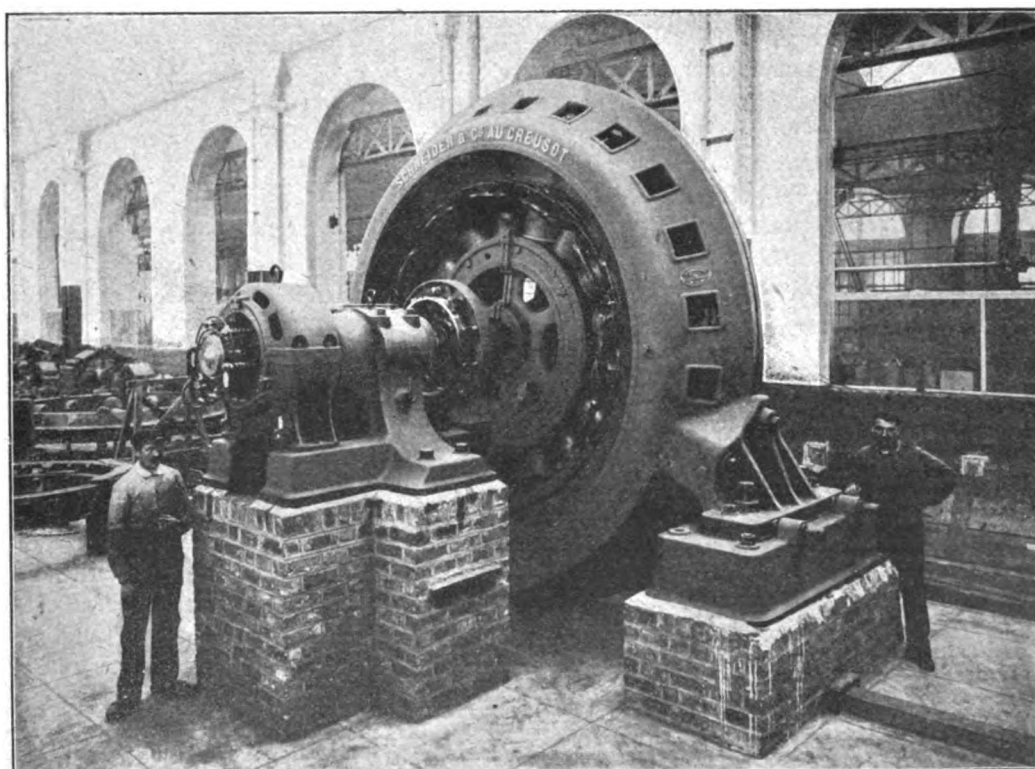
Vue d'ensemble d'un alternateur monté pour les essais.
